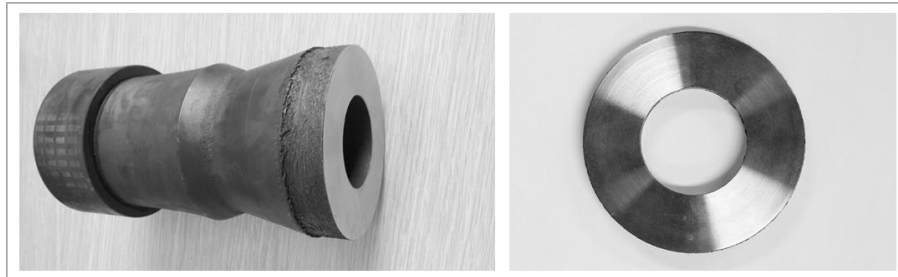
Bohrungsdruckprobe (links) nach Präparation des Ringsegmentes (rechts)
